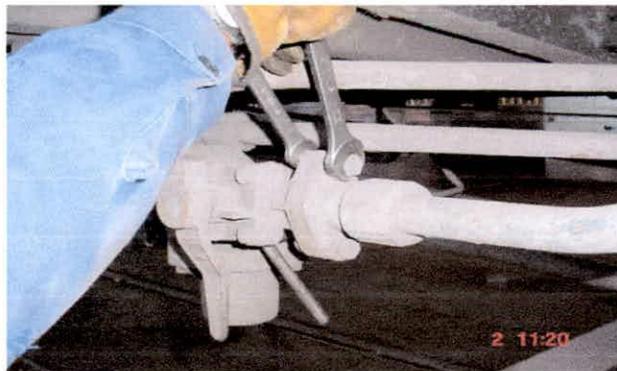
Afloje de tornillos de la brida de entrada de aire de la tubería
